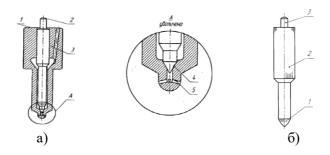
Места износа рабочих поверхностей распылителя а) 1-торец корпуса распылителя; 2-торец хвостовика иглы; 3-направляющая поверхность корпуса распылителя; 4-запорный конус корпуса распылителя; 5-распыливающие отверстия; б) игла распылителя форсунки: 1 — запорный конус распылителя; 2 — цилиндрическая направляющая поверхность иглы распылителя; 3 — хвостовик иглы распылителя.
